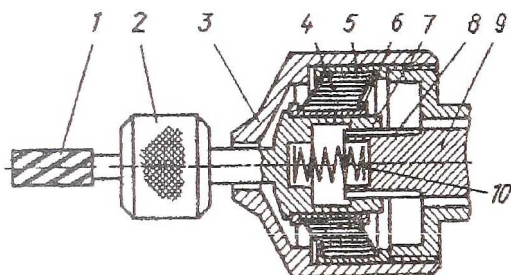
«Плавающая» опора ротора виброинструмента: 1 - режущий инструмент; 2 - шпindelь; 3 - корпус; 4 - упругодемпфирующий спиральный элемент; 5, 6 - неподвижный и подвижный диски; 7 - промежуточный элемент; 8 - шлицевое соединение; 9 - ротор; 10 - задатчик осевой нагрузки
